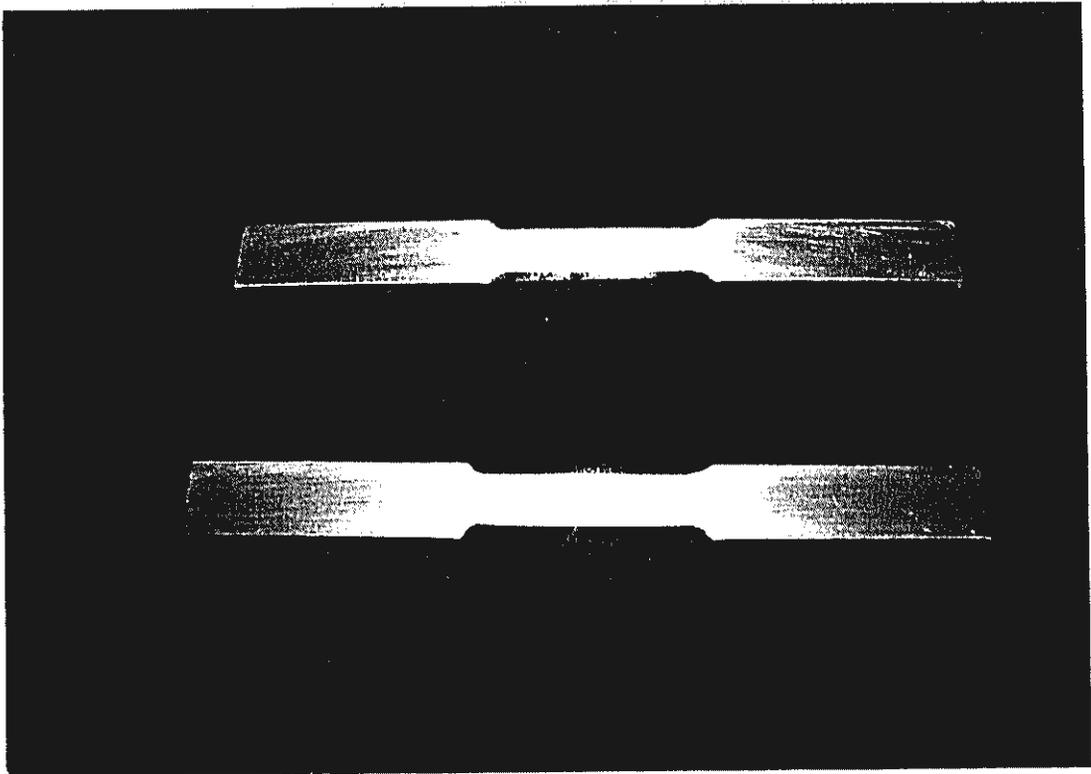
Fotografía de las Probetas para el Ensayo de Tracción
